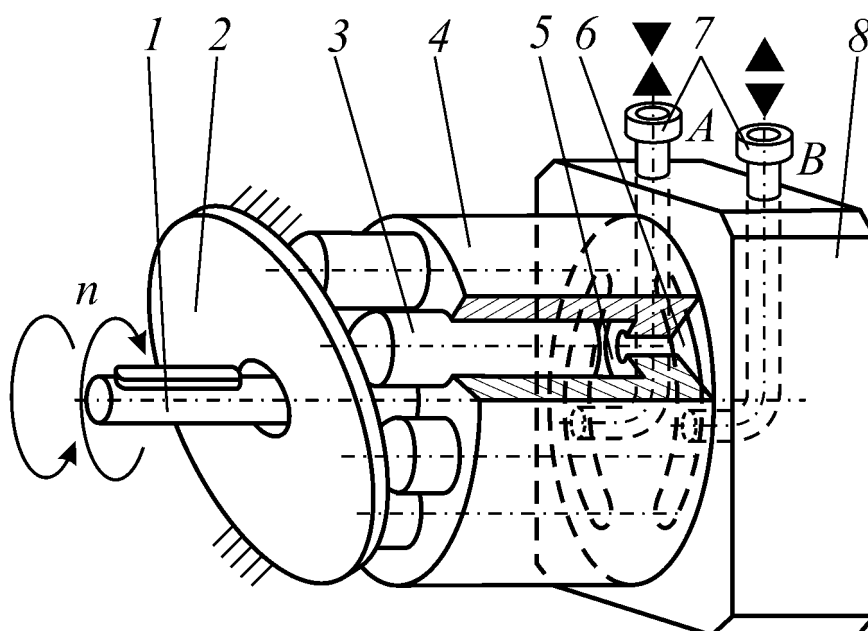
Схема нерегулируемого аксиально-поршневого гидромотора с наклонным диском: 1 – вал; 2 – наклонный диск; 3 – поршень (плунжер); 4 – блок цилиндров; 5 – рабочая камера в цилиндре (отверстии); 6 – серпообразные распределительные отверстия; 7 – присоединительные штуцеры; 8 – задняя крышка с распределительными отверстиями
